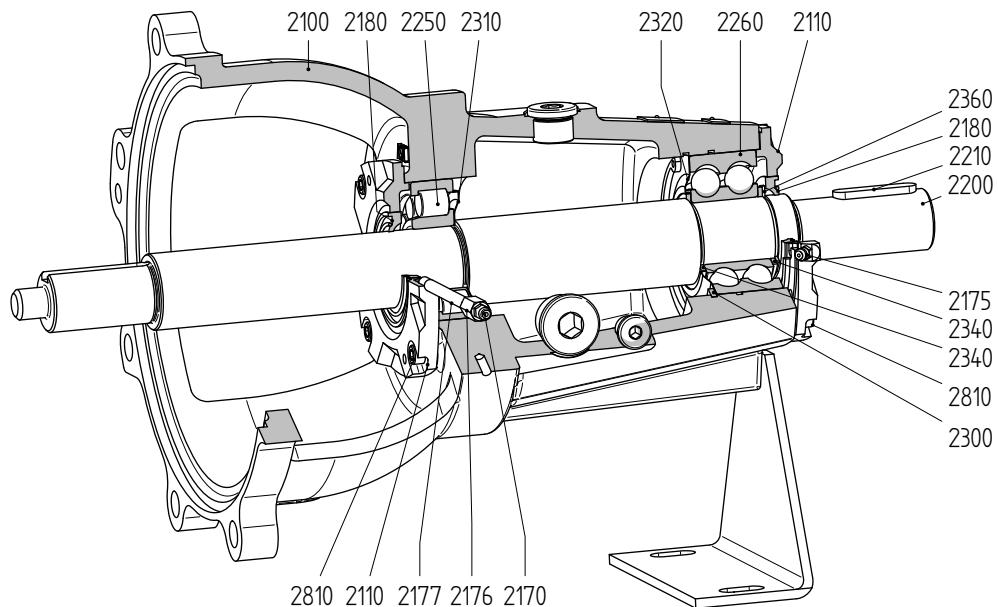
Подшипник L2 (усиленный, с консистентной смазкой)
